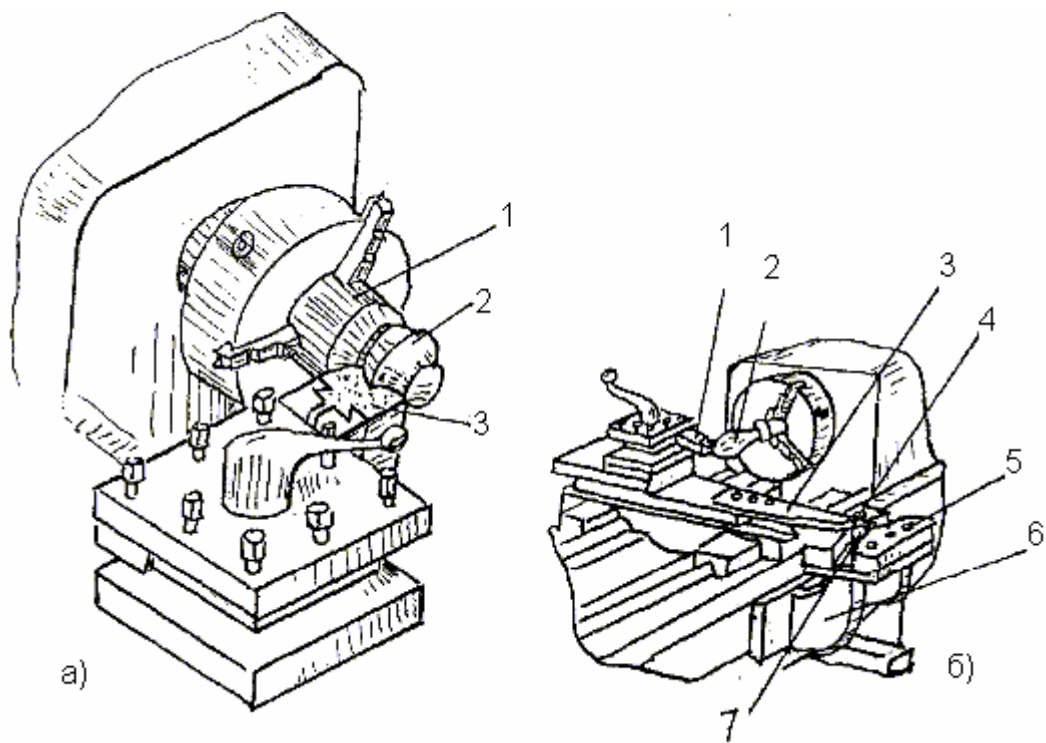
Схеми обробки фасонних поверхонь на токарному верстаті різцем:
